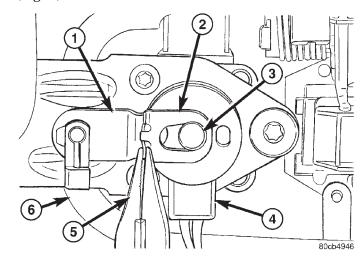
Desmontaje e instalación del conmutador de cilindro de cerradura-Característico
